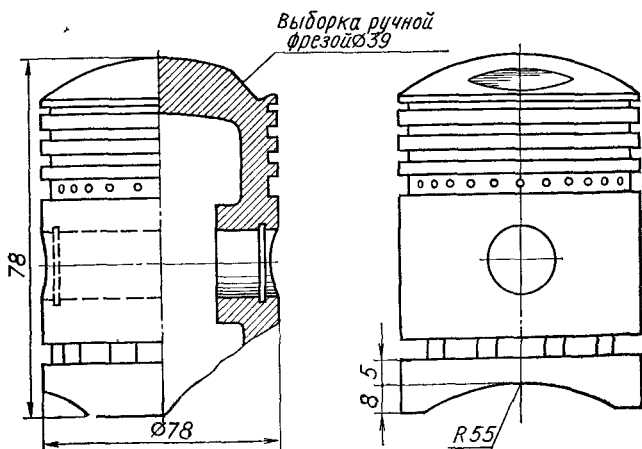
Поршень К-650, подготовленный к установке на двигатель мотоцикла М-63
